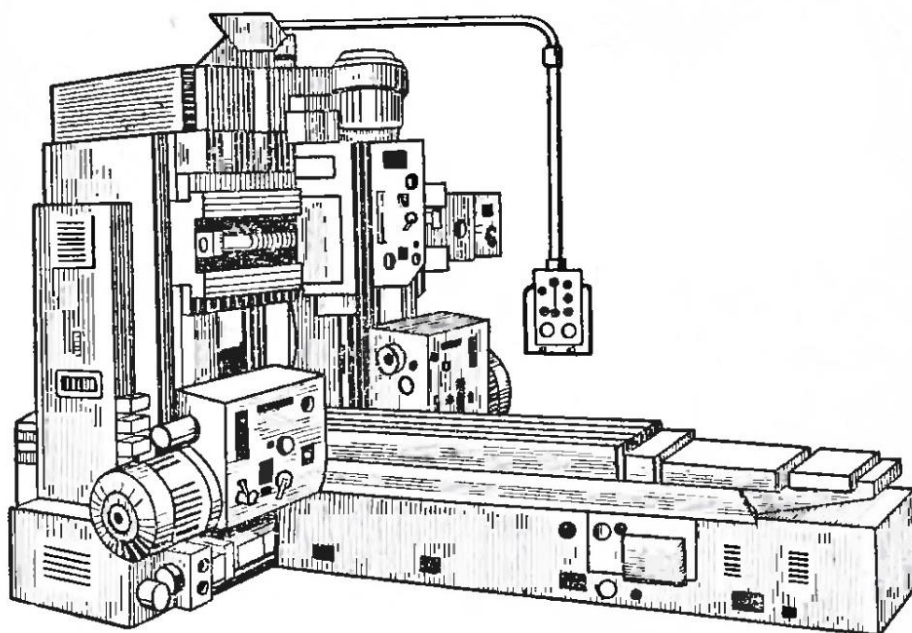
Двухстоечный продольно-фрезерный станок
